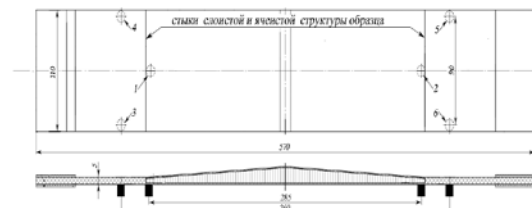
Форма и габаритные размеры конструктивно-подобного образца, места установки преобразователей *UT-1000* (1-2) и *R15-α* (3-6) на тыльной поверхности
